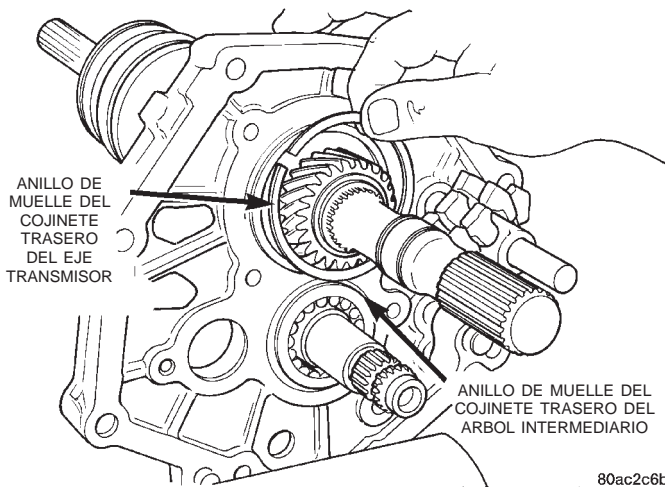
Desmontaje del anillo de muelle del cojinete trasero del eje transmisor
